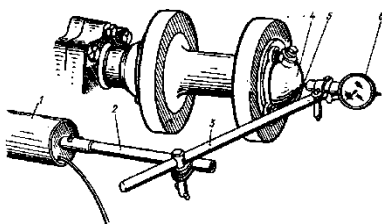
Вимірювання осьового зазору в підшипниках підтримувального ролика (колеса):
